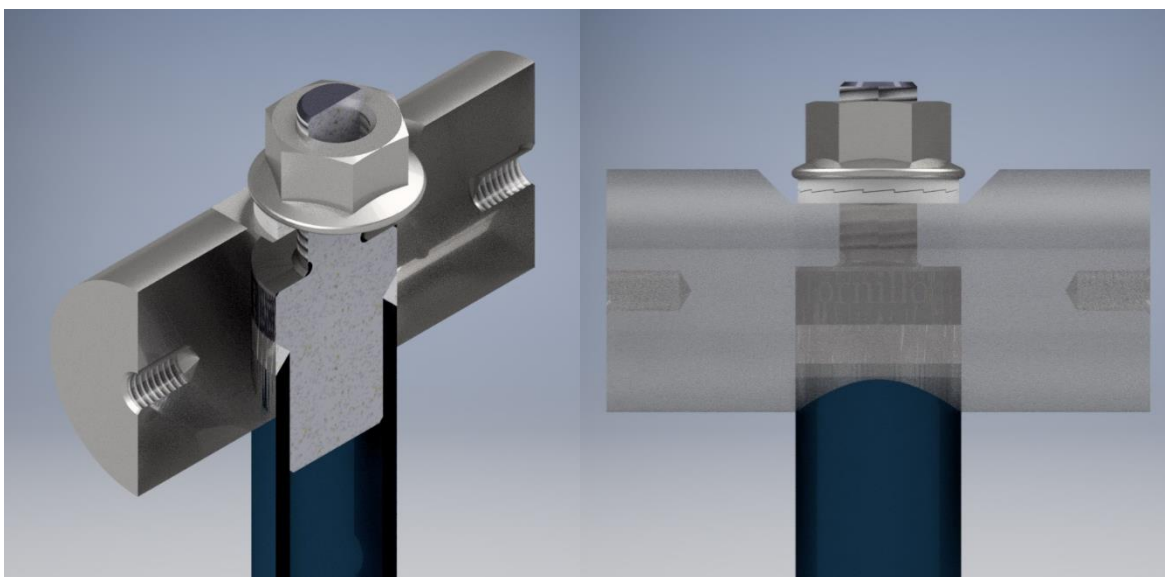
Primera propuesta tipo soldadura de mango tipo tornillo y tuerca de sujeción.
